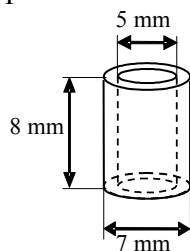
Géométrie des éprouvettes de caractérisation mécanique
